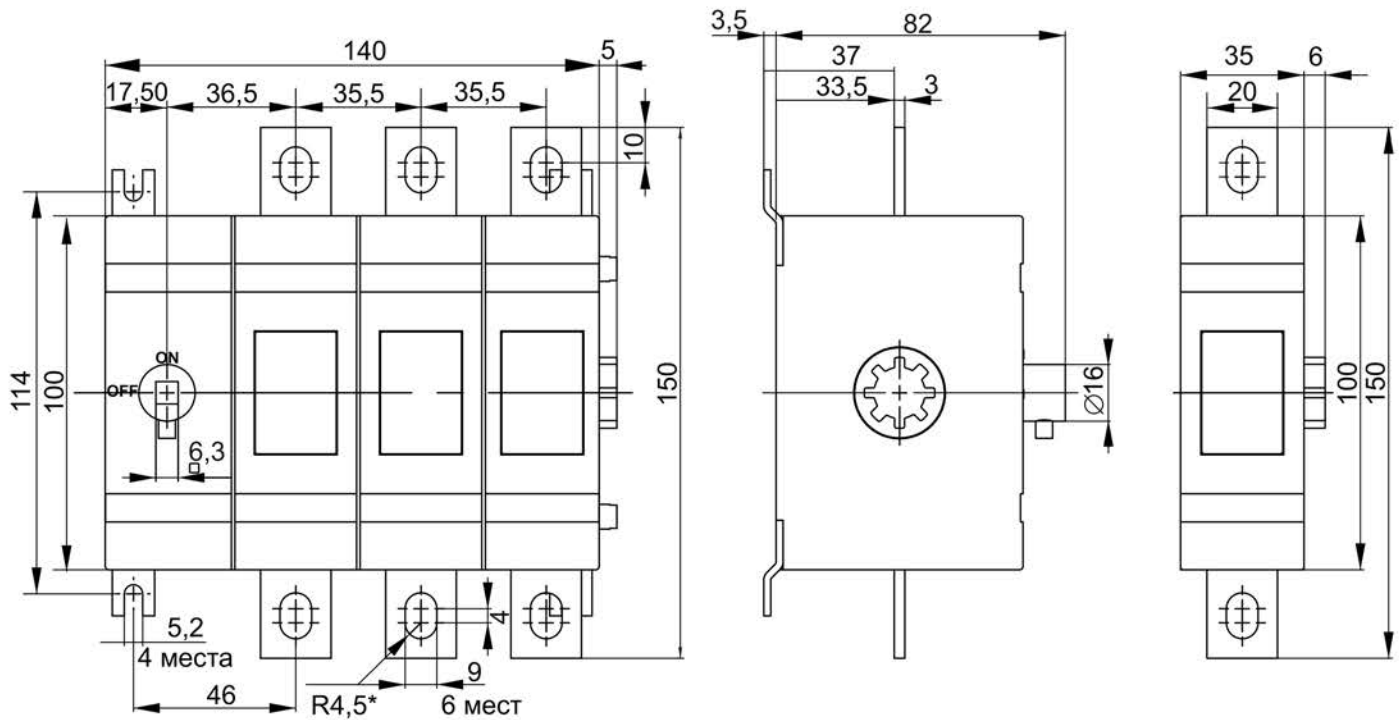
Габаритные, установочные и присоединительные размеры ВРК 160–250 А и дополнительного силового полюса 160–250 А / Figure 1 – Overall, mounting and connection dimensions of VRK 160–250 A and additional power pole 160–250 A
